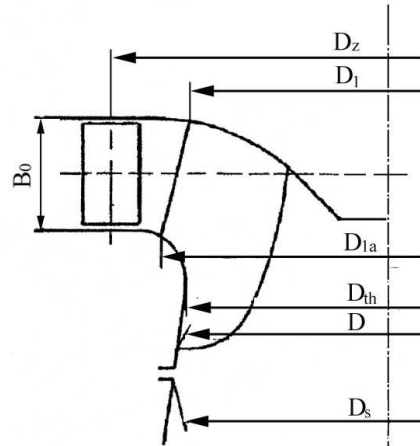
8 Dimensiunile principale ale unui rotor de turbină radial axială [126]
